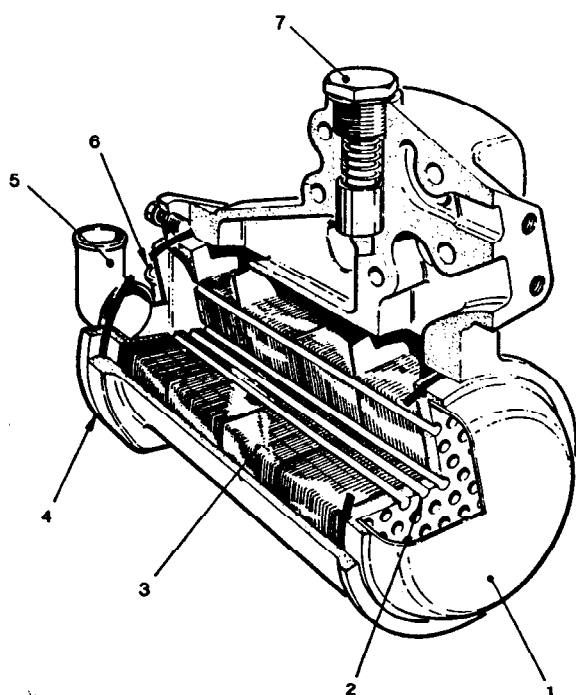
Enfriador de aceite. 1 tapa de extremo, 2 tubos para líquido enfriador, 3 aletas, 4 tapa de extremo, 5 y 6 conexiones para mangueras de líquido enfriador, 7 válvulas de desahogo
